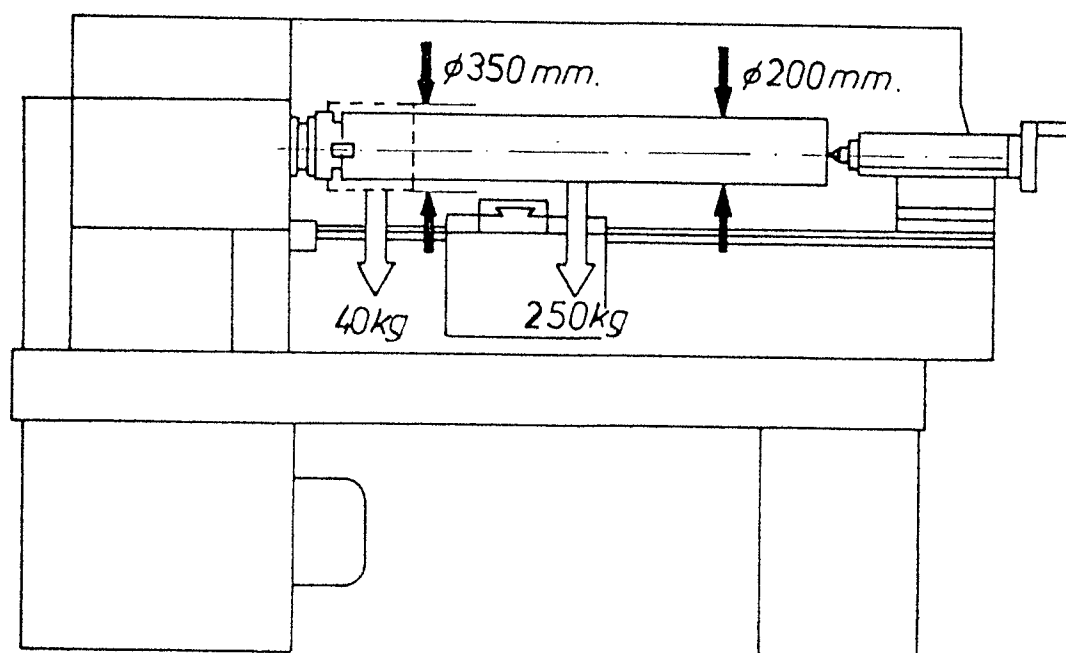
Dimensions et masses maxima des pièces à usiner
